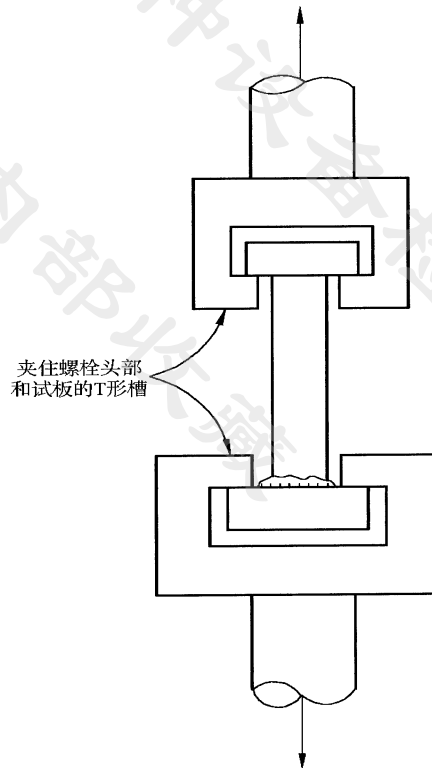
螺柱电弧焊拉伸试验推荐装置
